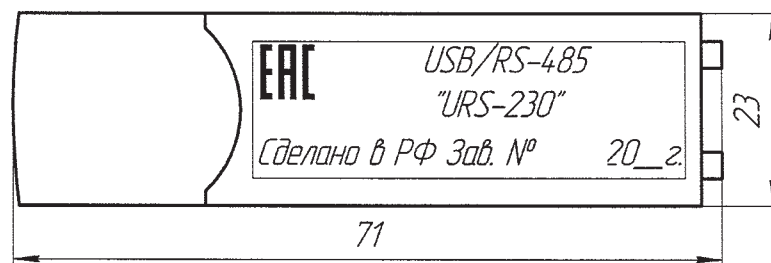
Внешний вид ПИ с габаритными размерами
